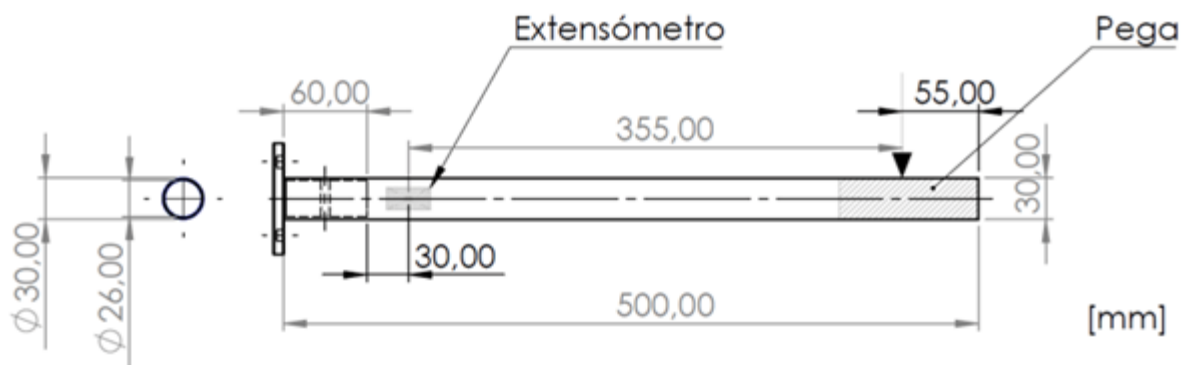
Esquema da viga do Dispositivo de Apoio.
